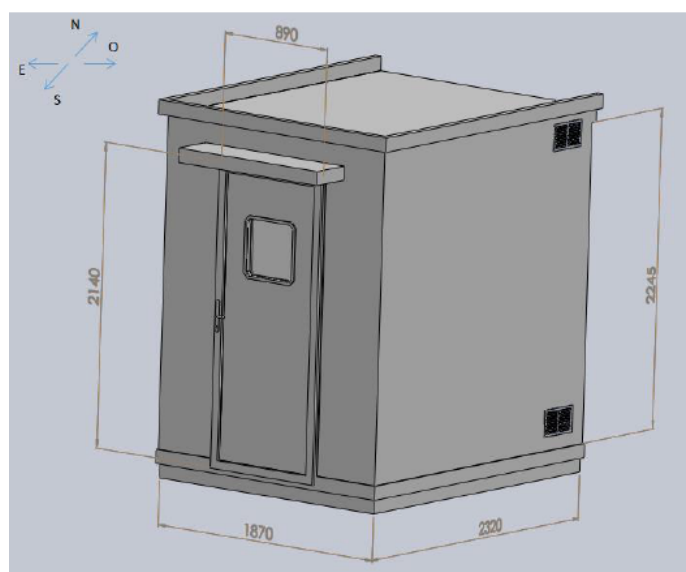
Desenho tridimensional da casa das máquinas com as dimensões mais relevantes [15].
